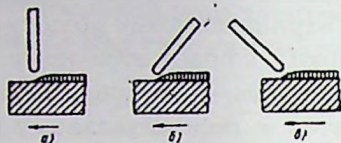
Различное положение электродов при сварке:
